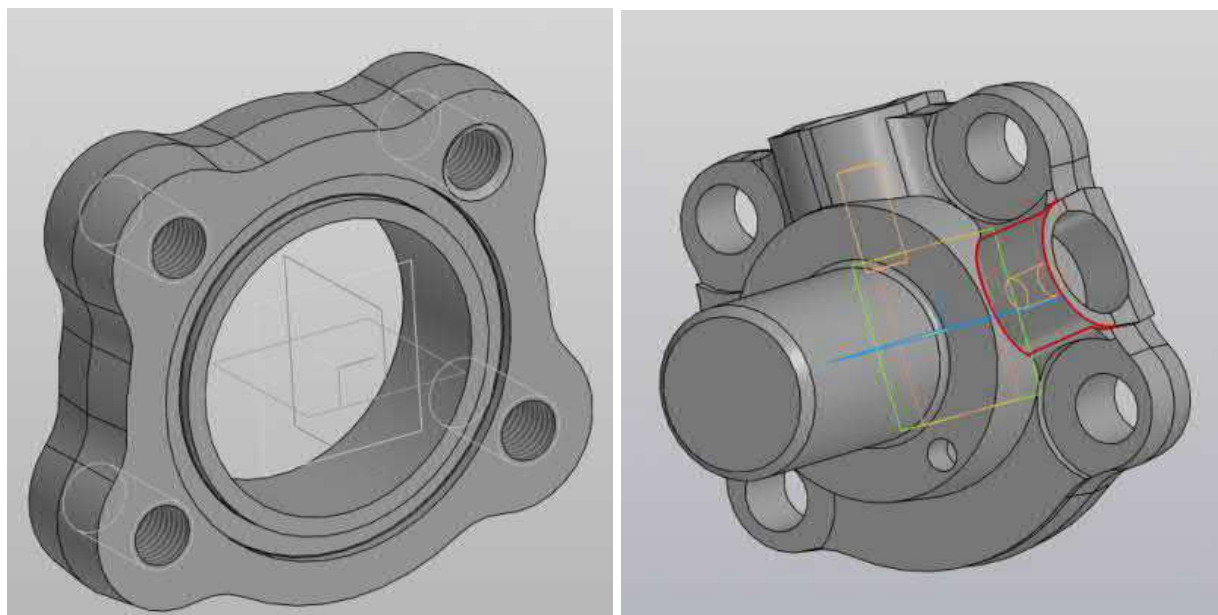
3D-модели деталей входящих в сборочный узел
